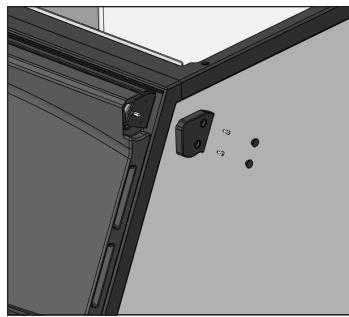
Explosionsansicht der Endkappe der Türhalterung, der Schrauben und Schraubekappen.
